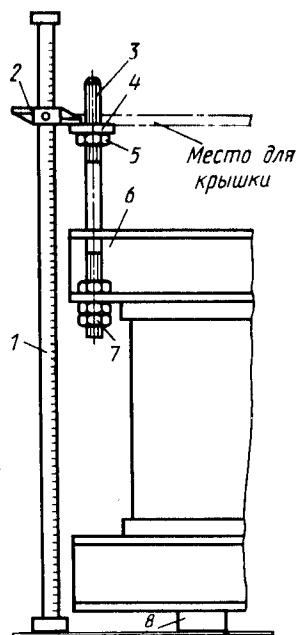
Определение высоты установки крышки бака на подъемных шпильках рейкой
